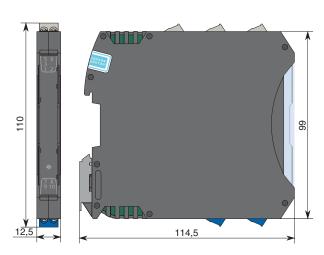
Габаритные размеры барьера в корпусе шириной 12,5 мм с разъемами с винтовыми клеммниками
